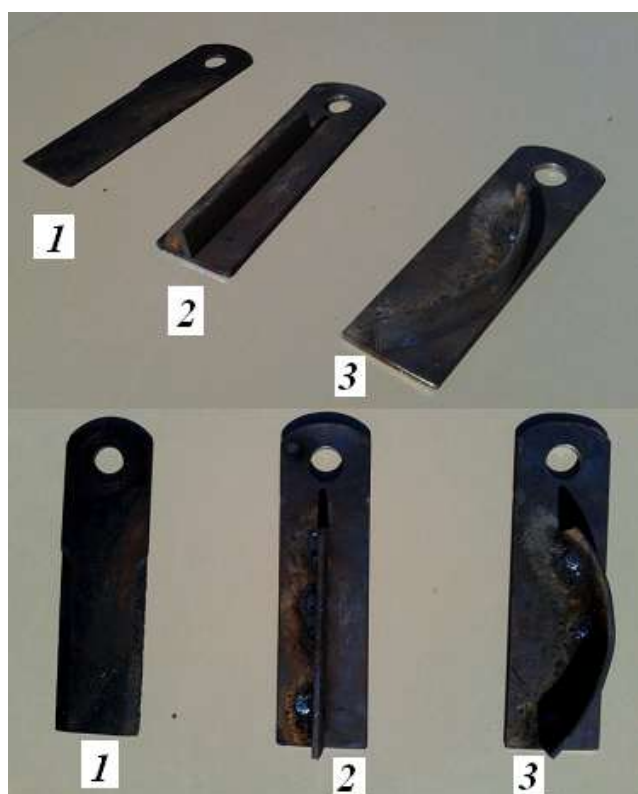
Ножи лабораторной косилки. 1 - стандартные, 2 - с пластиной под прямым углом, 3 - с криволинейной пластиной
